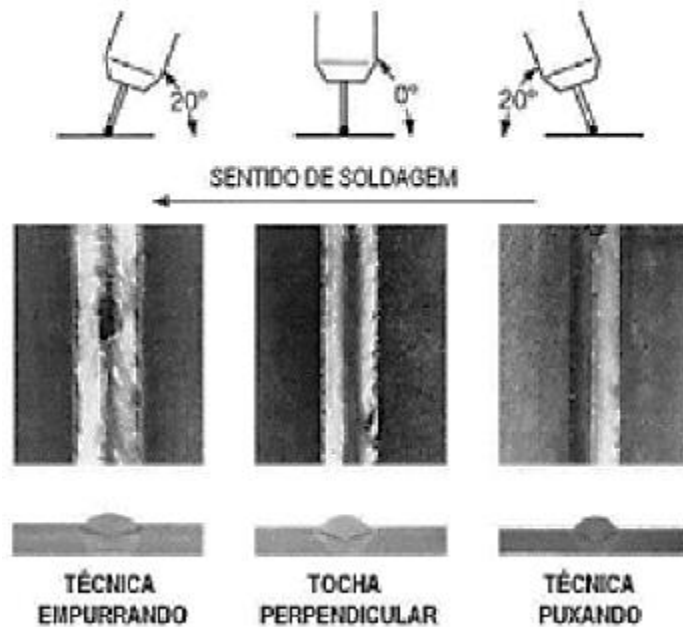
Efeito da angulação e técnica na penetração da solda [29].
